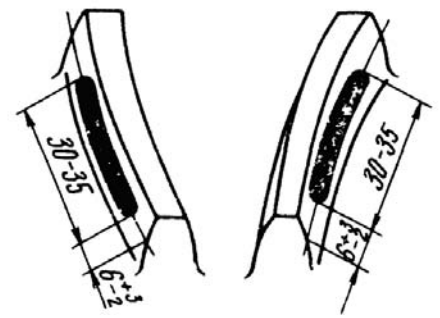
Нормальное положение пятна контакта в зацеплении конических зубчатых колес главной передачи
